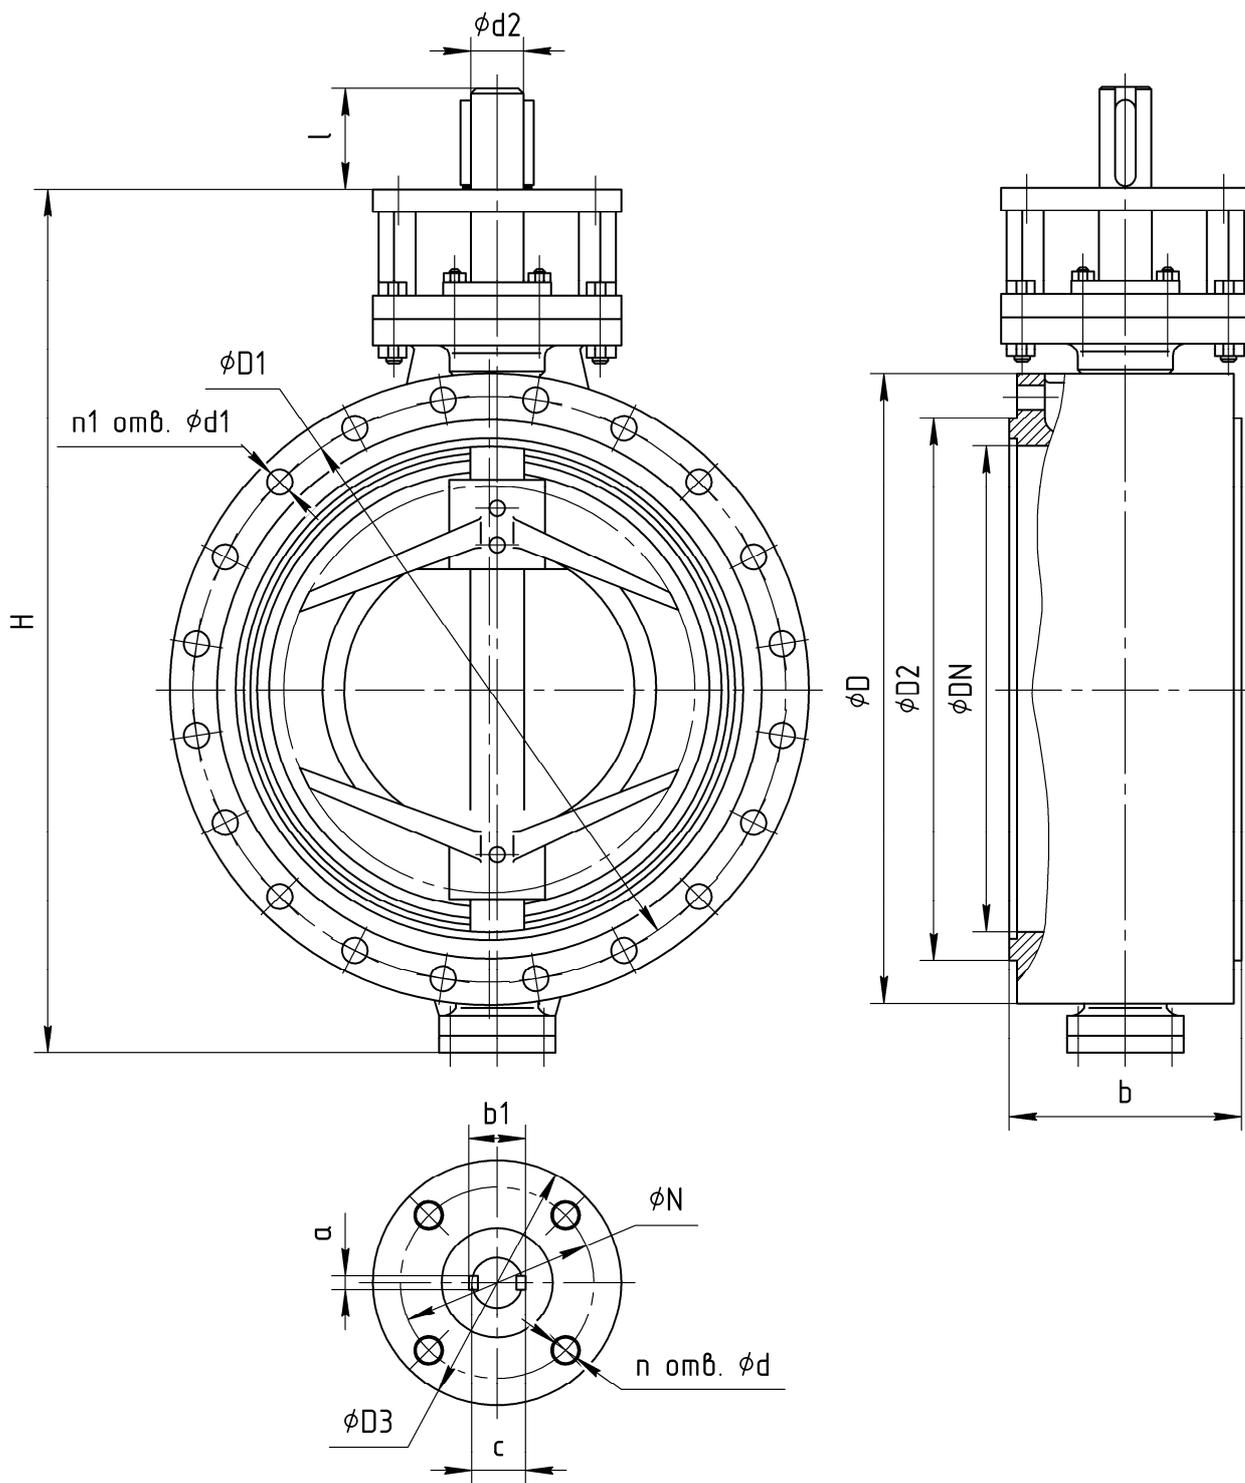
Габаритные и присоединительные размеры затвора с тройным эксцентриситетом
